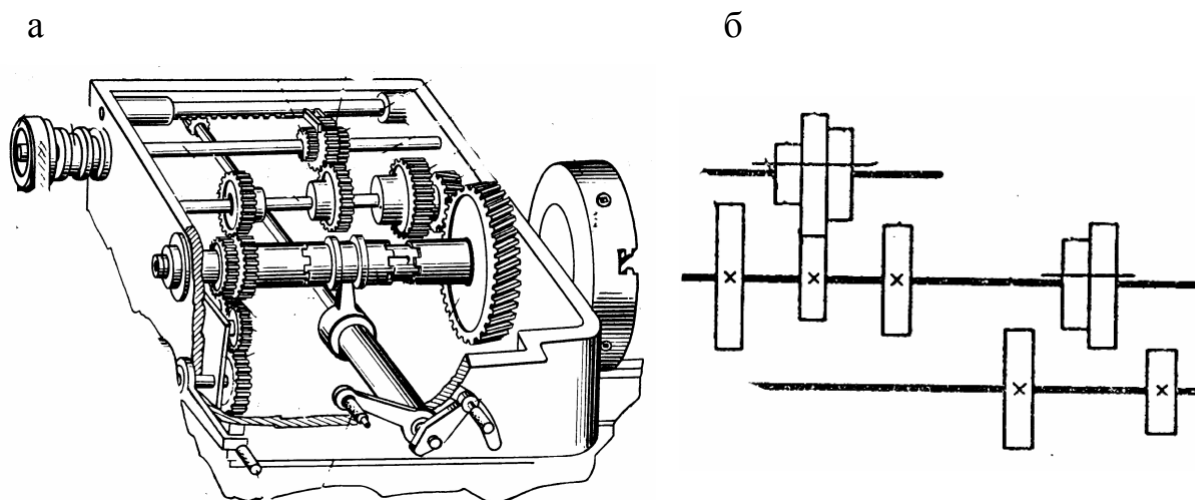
Коробка скоростей токарно-винторезного станка
